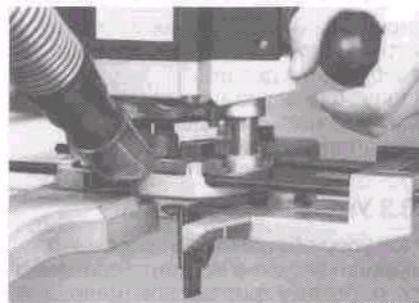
Фрезерование по фигурному краю. Параллельный упор фрезерной машины с ведущим роликом 30 360
